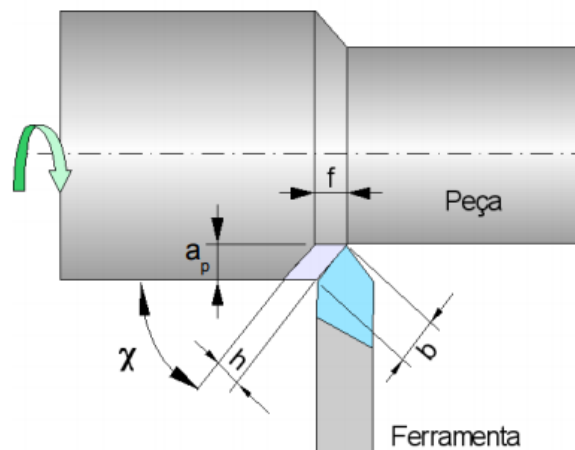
Grandezas no processo de usinagem. (Fundamentos dos processos de usinagem, 2010).
